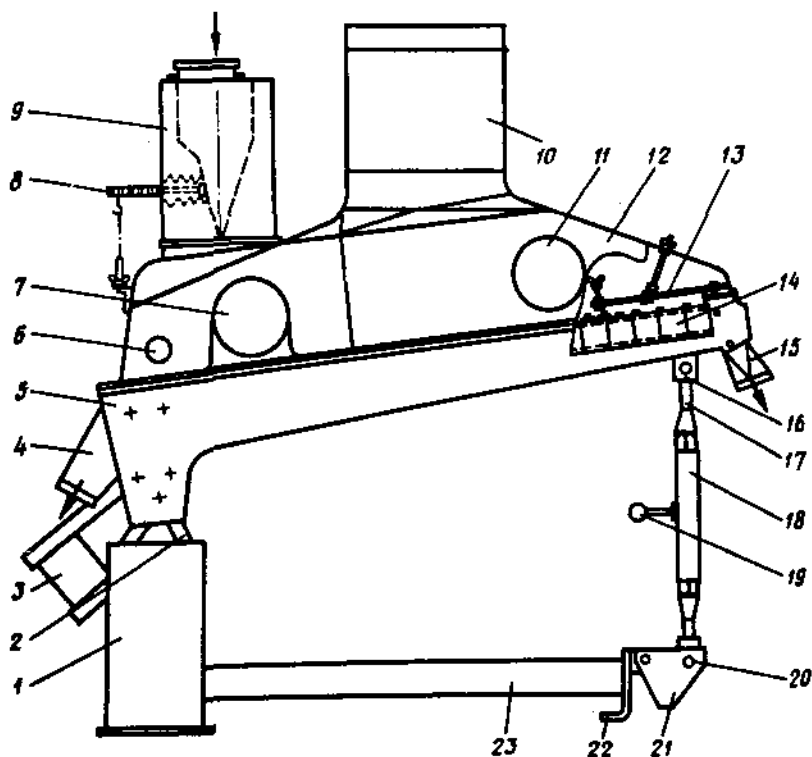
Схема камнеотборника РЗ-БКТ-100
